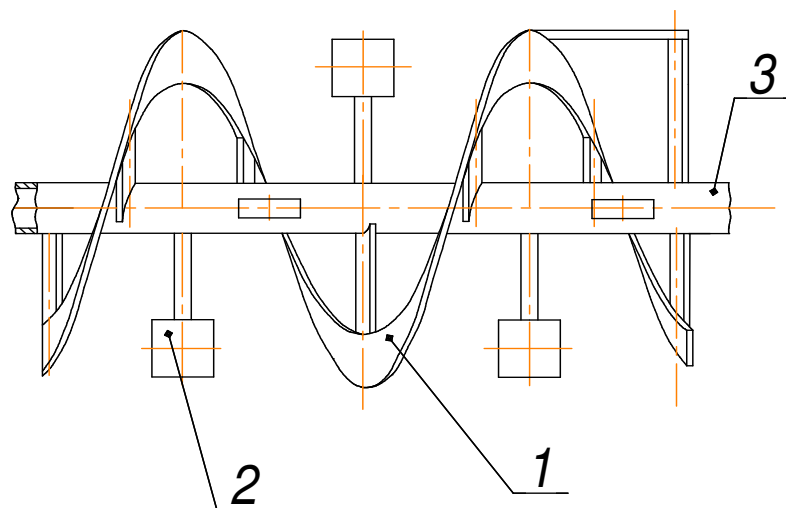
Схема робочого органа стрічково-лопатєвого змішувача:
